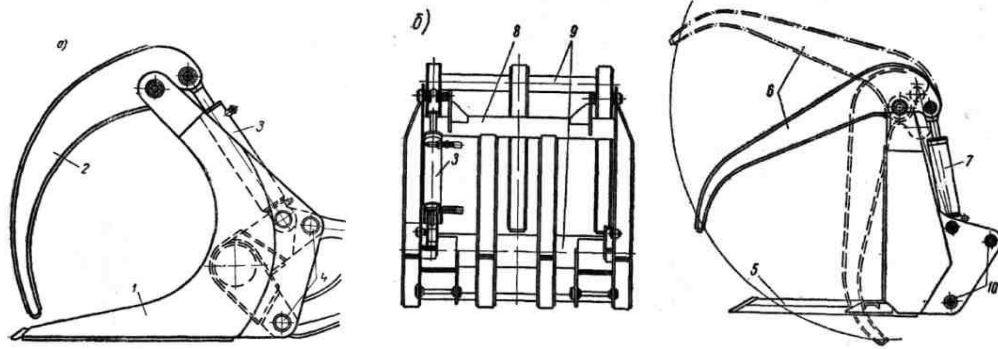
Щелепний захоплювач: а – для довгомірних вантажів; б – для штучних вантажів: 1 – нижня щелепа; 2 – рухома верхня щелепа; 3 – гідроциліндр стулення і розмикання щелеп; 4 – провушини; 5 – стрижні вил; 6 – рухома верхня щелепа; 7 – гідроциліндр; 8 – поперечина; 9 – поперечні труби; 10 – провушини
